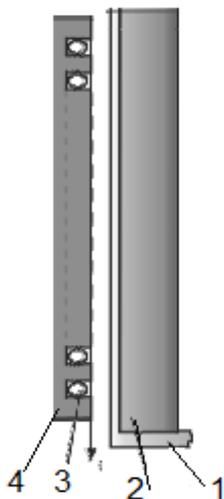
Схематическое изображение печь – перемешиватель: 1-тигель; 2.- расплав металла; 3,4- обмотка и магнитопровод перемешивателя.
